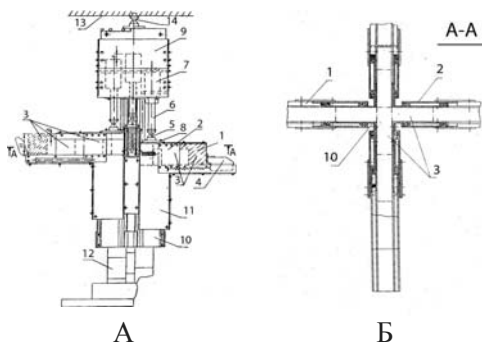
а. Загальний вид пристрою для монтажу надважких конструкцій Рис . 6-б. Розріз по А-А (вид зверху)
